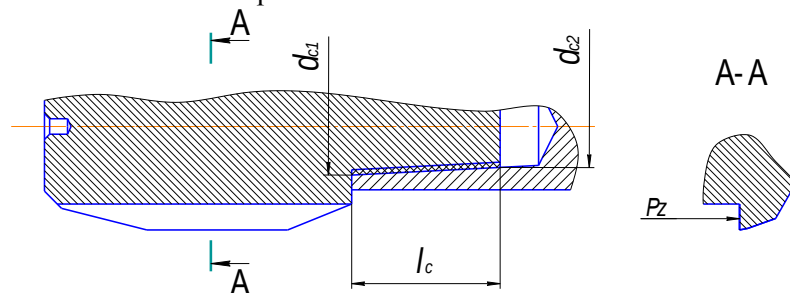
Соединение твердосплавной вставки с хвостовиком развертки
